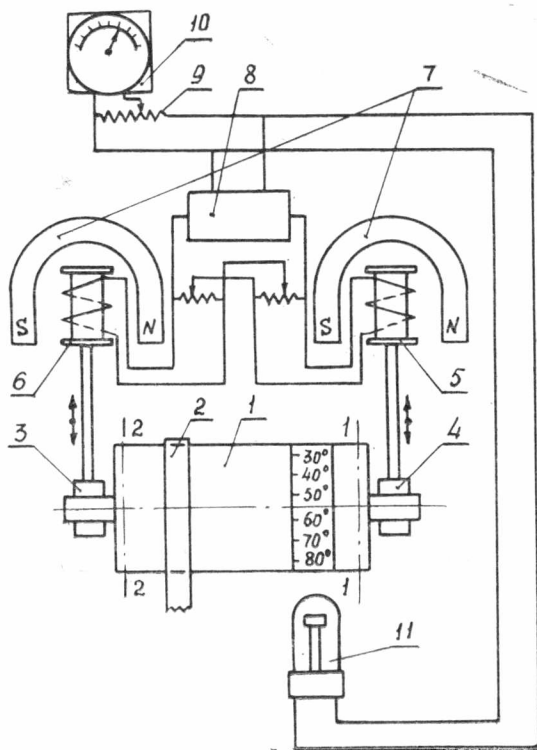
Схема балансировочной машины: 1 — ротор; 2 — ремень приводной; 3 — опора левая; 4 — опора правая; 5, 6 — катушки датчиков, 7 — постоянные магниты; 8 — усилитель; 9 — сопротивление; 10 — индикатор значения дисбаланса
